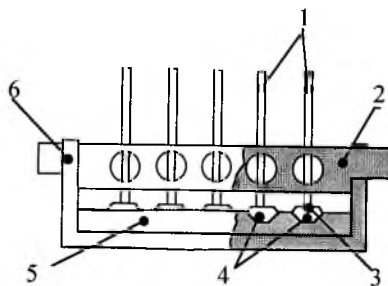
Схема приспособления для пайки стержней к кристаллам алмаза с помощью порошковых сплавов: 1 – стальные стержни; 2 – направляющая; 3 – порошковая композиция; 4 – кристаллы алмаза; 5 – графит; 6 – обойма.
